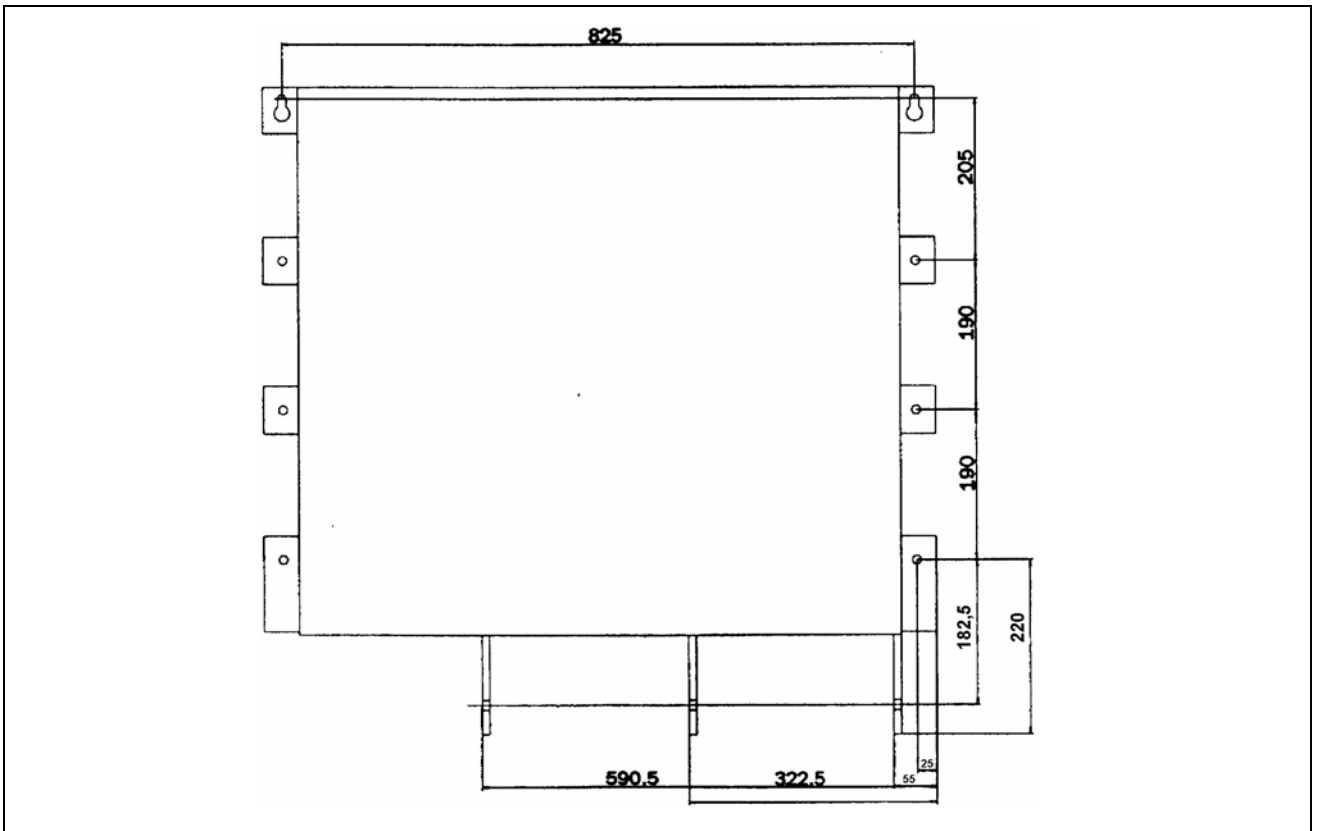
Размеры отверстий для шин MSF-1000 ... MSF-1400
